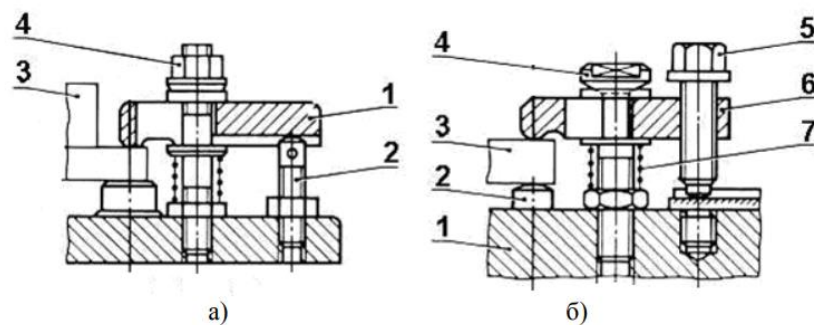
Застосування гвинтових затискачів для закріплення заготовок
